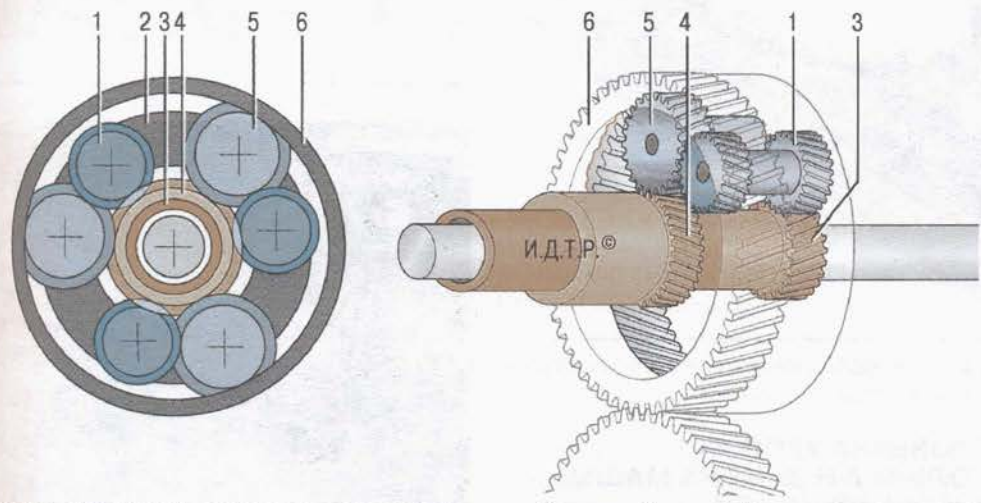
Планетарный редуктор системы Равинье: 1 – длинный сателлит; 2 – водило; 3 – малая солнечная шестерня; 4 – большая солнечная шестерня; 5 – короткий сателлит; 6 – коронная шестерня
